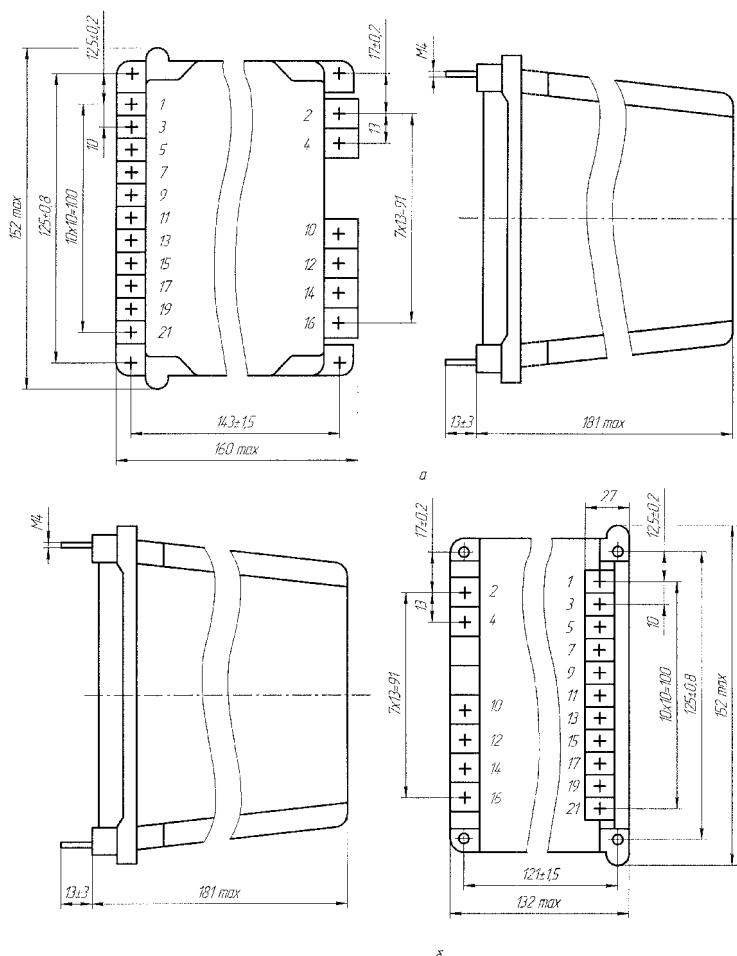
Габаритные, установочные, присоединительные размеры реле РТФ 8 и РТФ 9.
